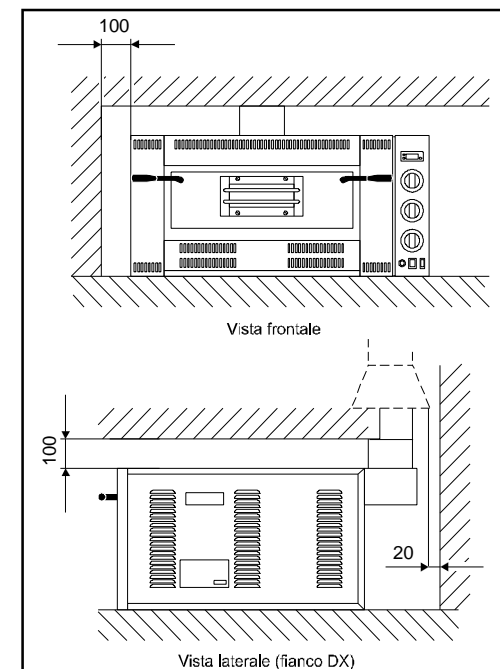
(Benötigte Mindestabmessungen für die Montage)
